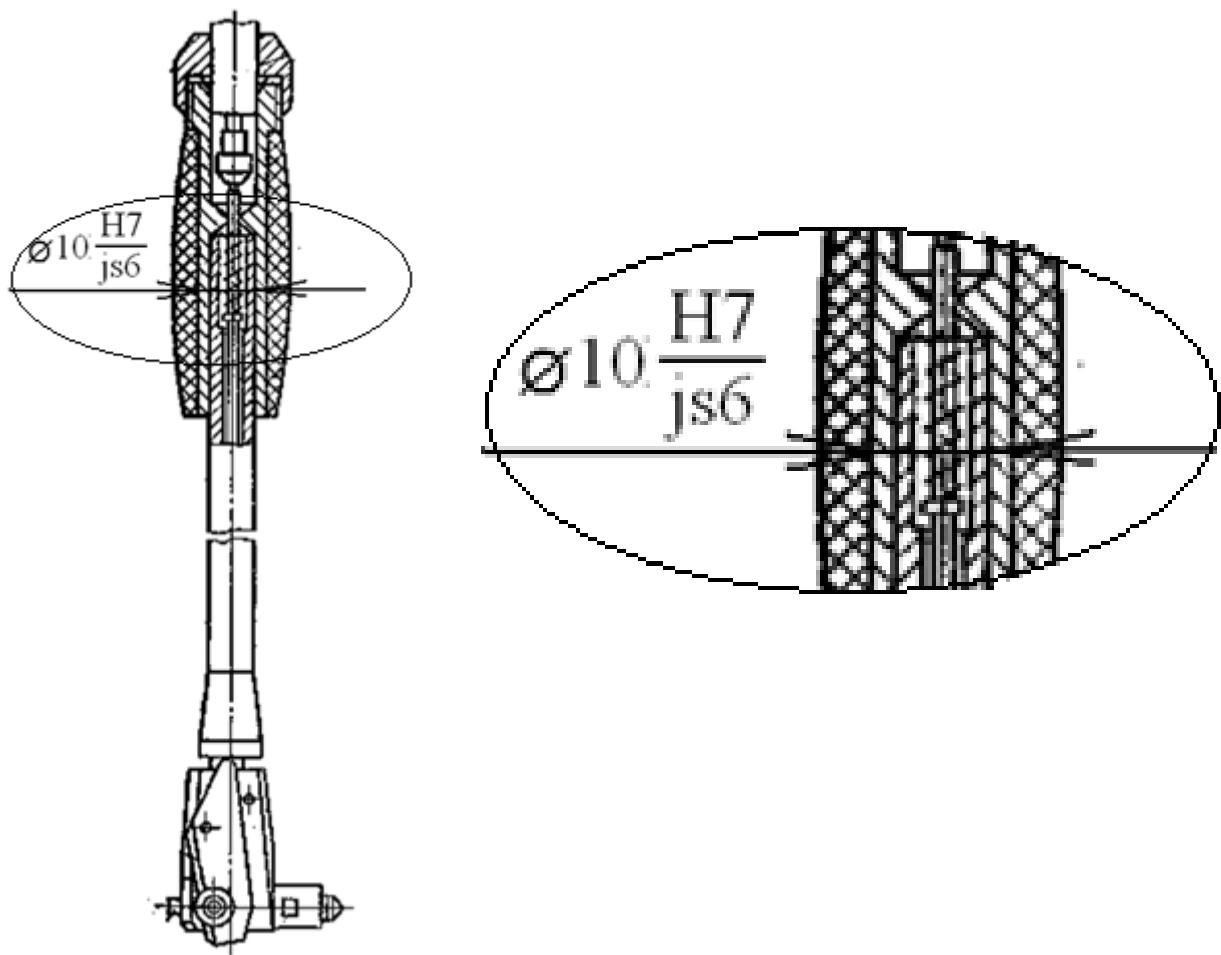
Направляющая втулка в корпус индикаторного нутромера
